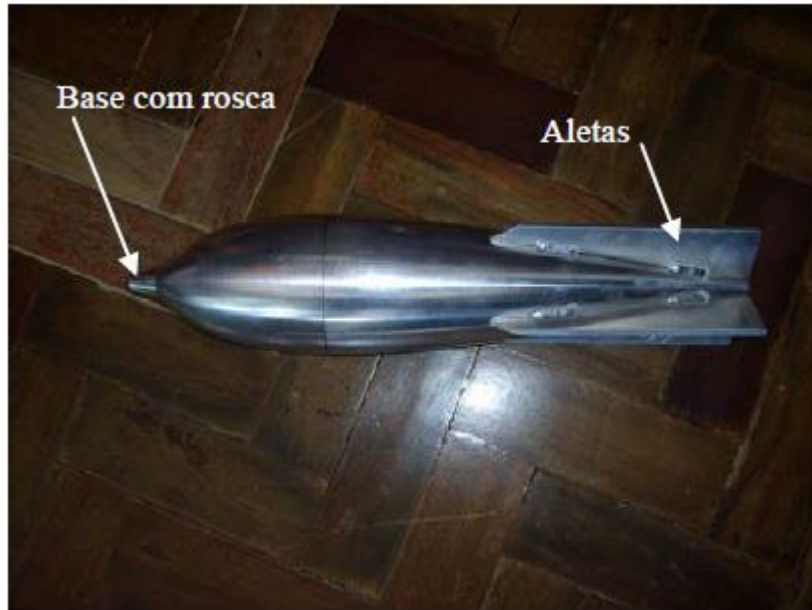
Corpo do penetrômetro usinado, com aletas direcionais soldadas.
